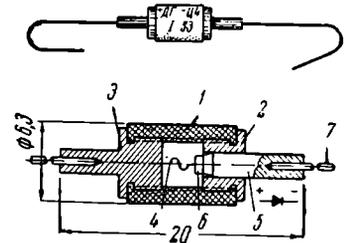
Внешний вид и разрез германиевого точечного детектора ДГ-Ц4 (размеры в миллиметрах). 1 — керамическая втулка; 2 и 3 — металлические фланцы; 4 — вольфрамовый зонд; 5 — кристаллодержатель; 6 — германиевый кристаллик; 7 — металлические выводы
